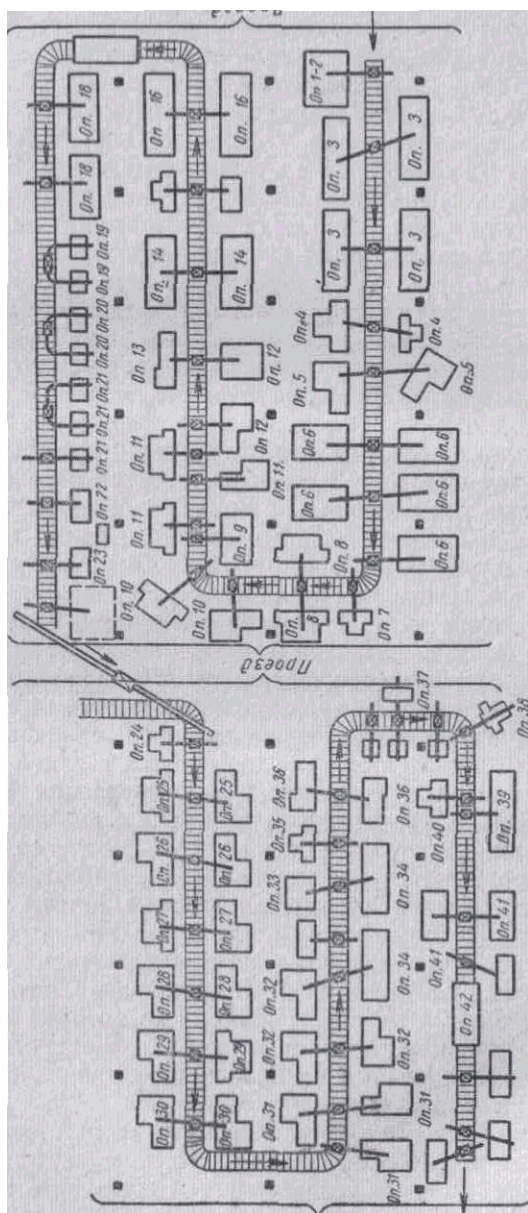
Расстановка оборудования поточной линии для изготовления коленчатого вала
